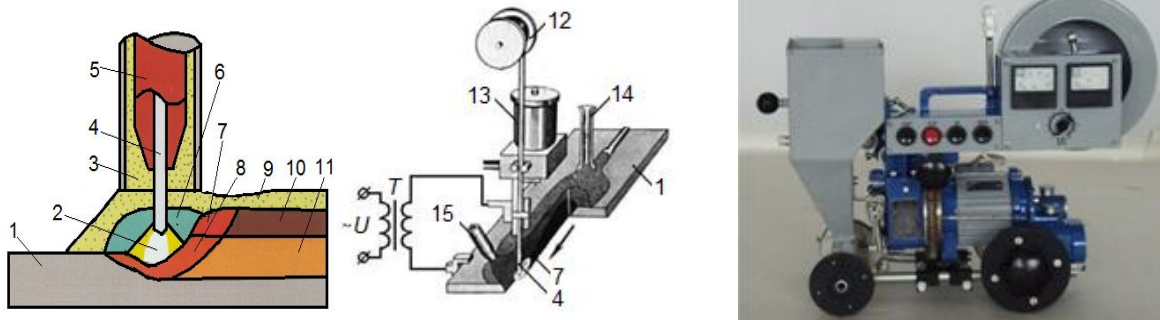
Електрозварювальні установки для електрошлакового зварювання: 1 – матеріали, що з'єднуються, 2 – електрична дуга; 3 – флюс; 4 – електрод; 5 – контактний наконечник; 6 – захисна атмосфера; 7 – розплавлений шлак; 8 – зварочна ванна; 9 – флюс; 10 – шлак, що застиг; 11 – метал, що зварився; 12 – бухта подачі дроту; 13 – привод; 14 – сопло для видалення шлаку; 15 – сопло для подачі флюсу
